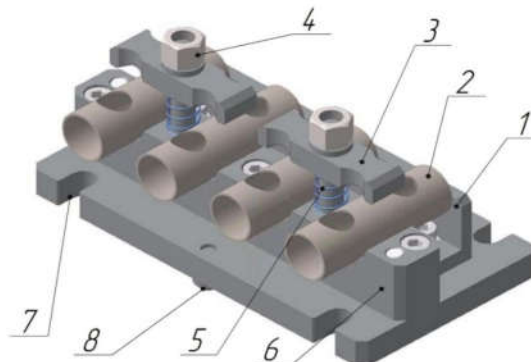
Пристосування для одночасної обробки 4-х труб:
